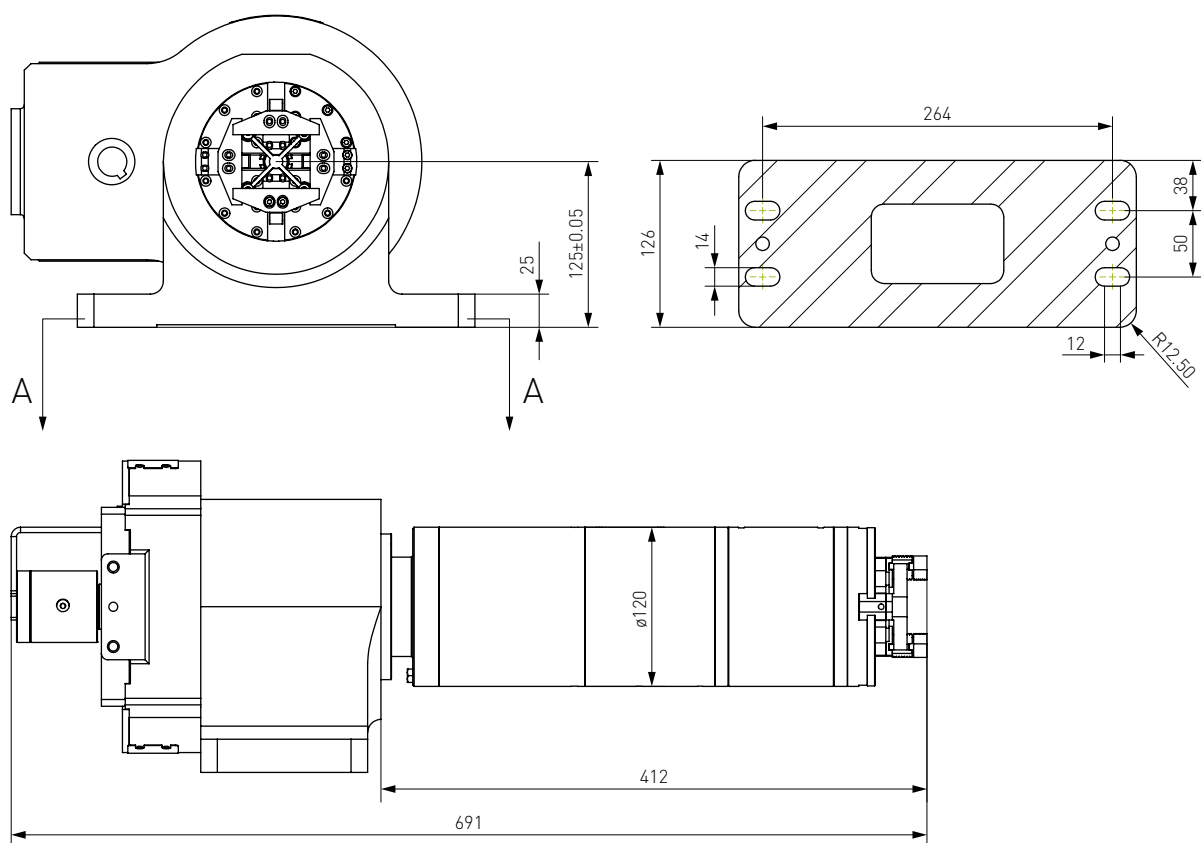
Габаритный чертеж патрона основного RKN-120C.
